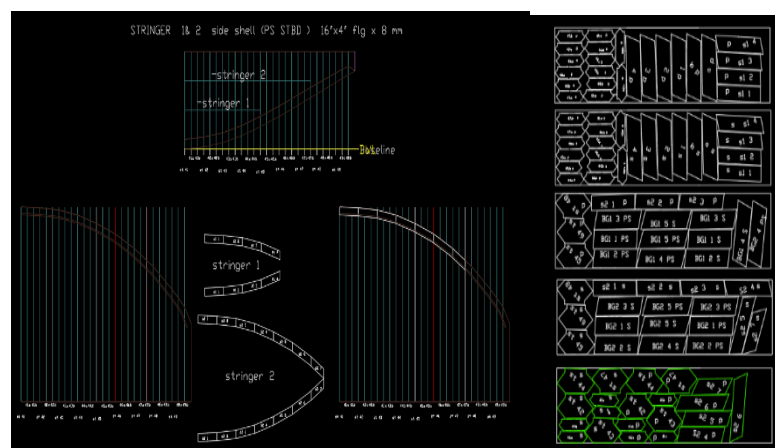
58 Nesting bottom girder dan ordinary frame
